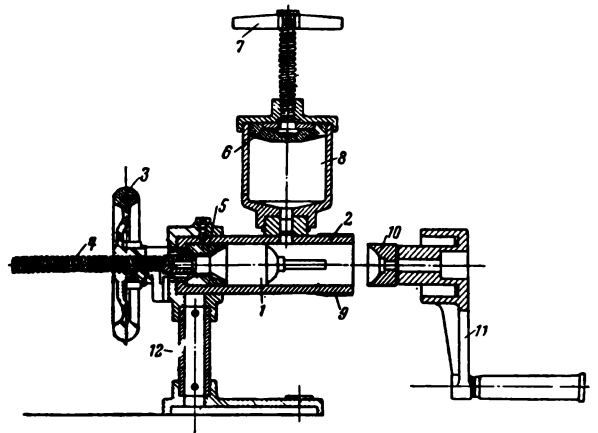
Пресс для опрессовки обмотки пластмассой.
